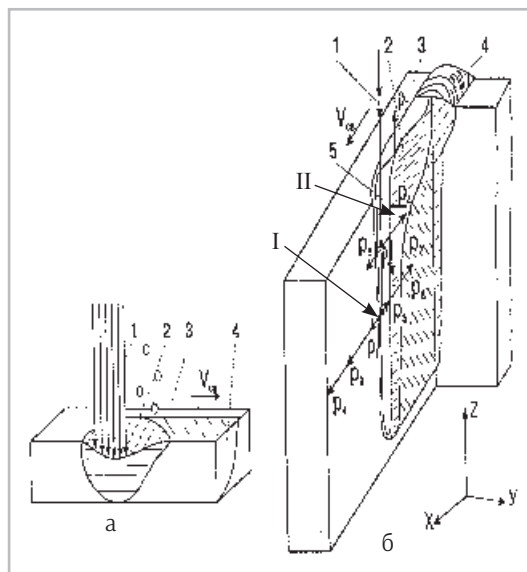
Продольно-поперечное сечение сварочной ванны со схемой давлений, воздействующих на жидкий металл: а — сварка низкоконцентрированным источником нагрева; б — сварка с глубоким проплавлением; 1 — сварочный пучок; 2 — расплавленный металл; 3 — свариваемый металл; 4 — сварной шов; 5 — пародинамический канал; I — передняя стенка канала; II — задняя стенка канала
